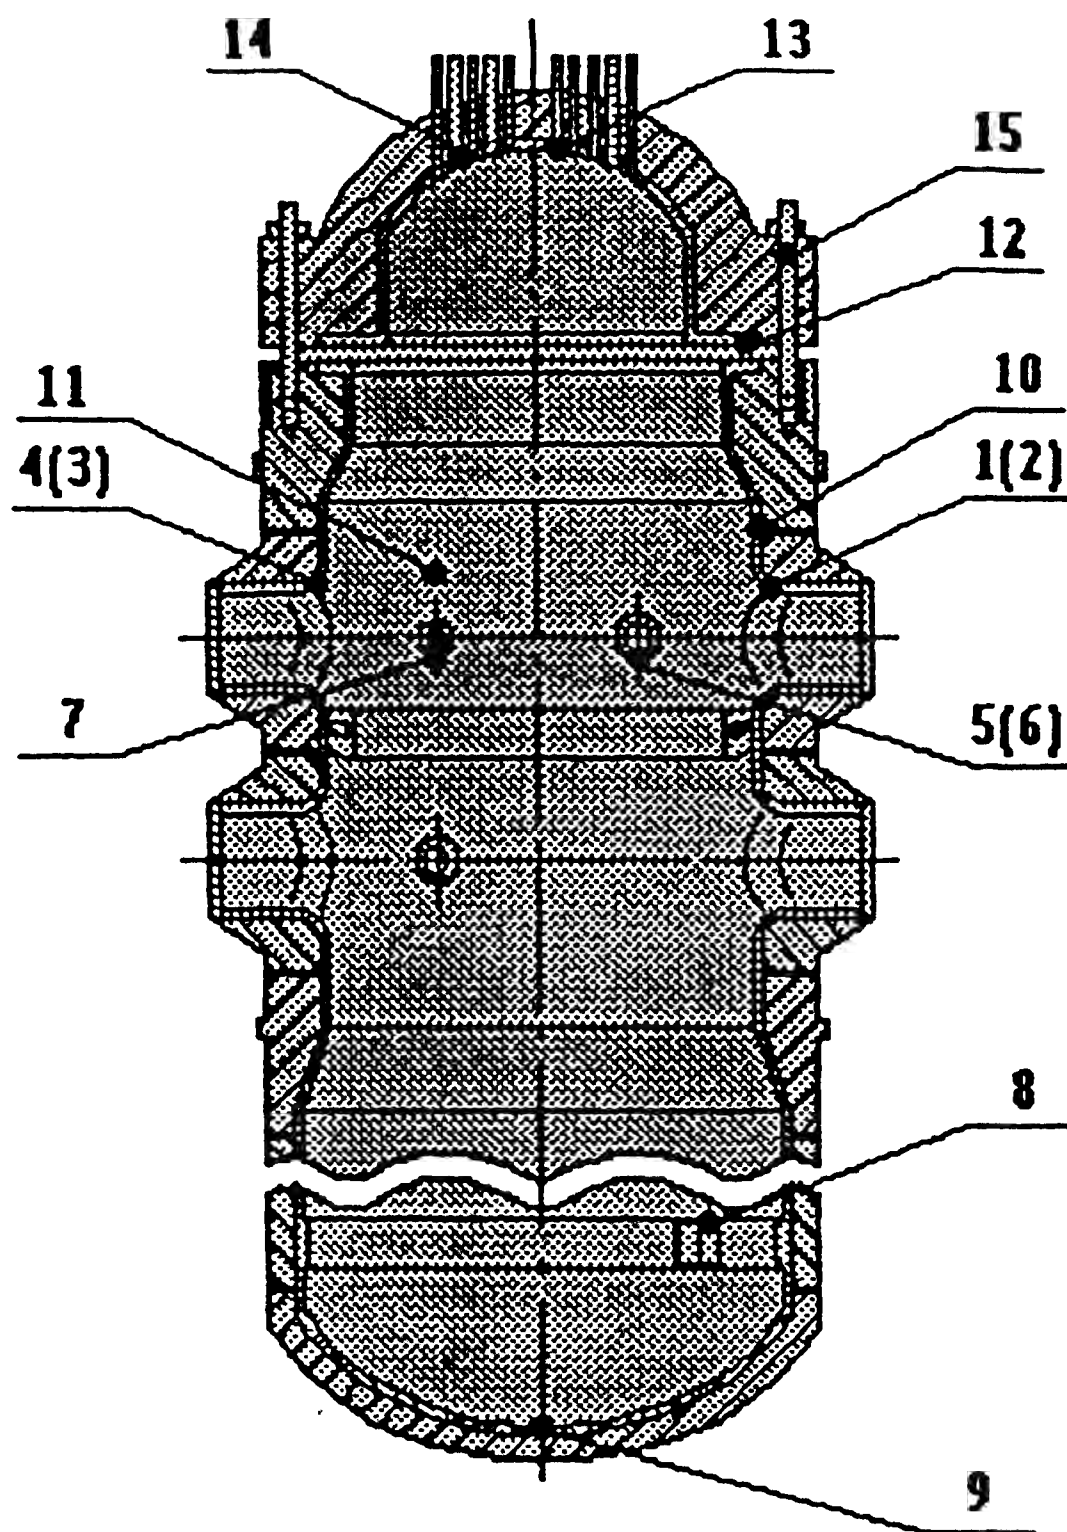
Контролируемые точки корпуса и крышки реактора ВВЭР-1000:
